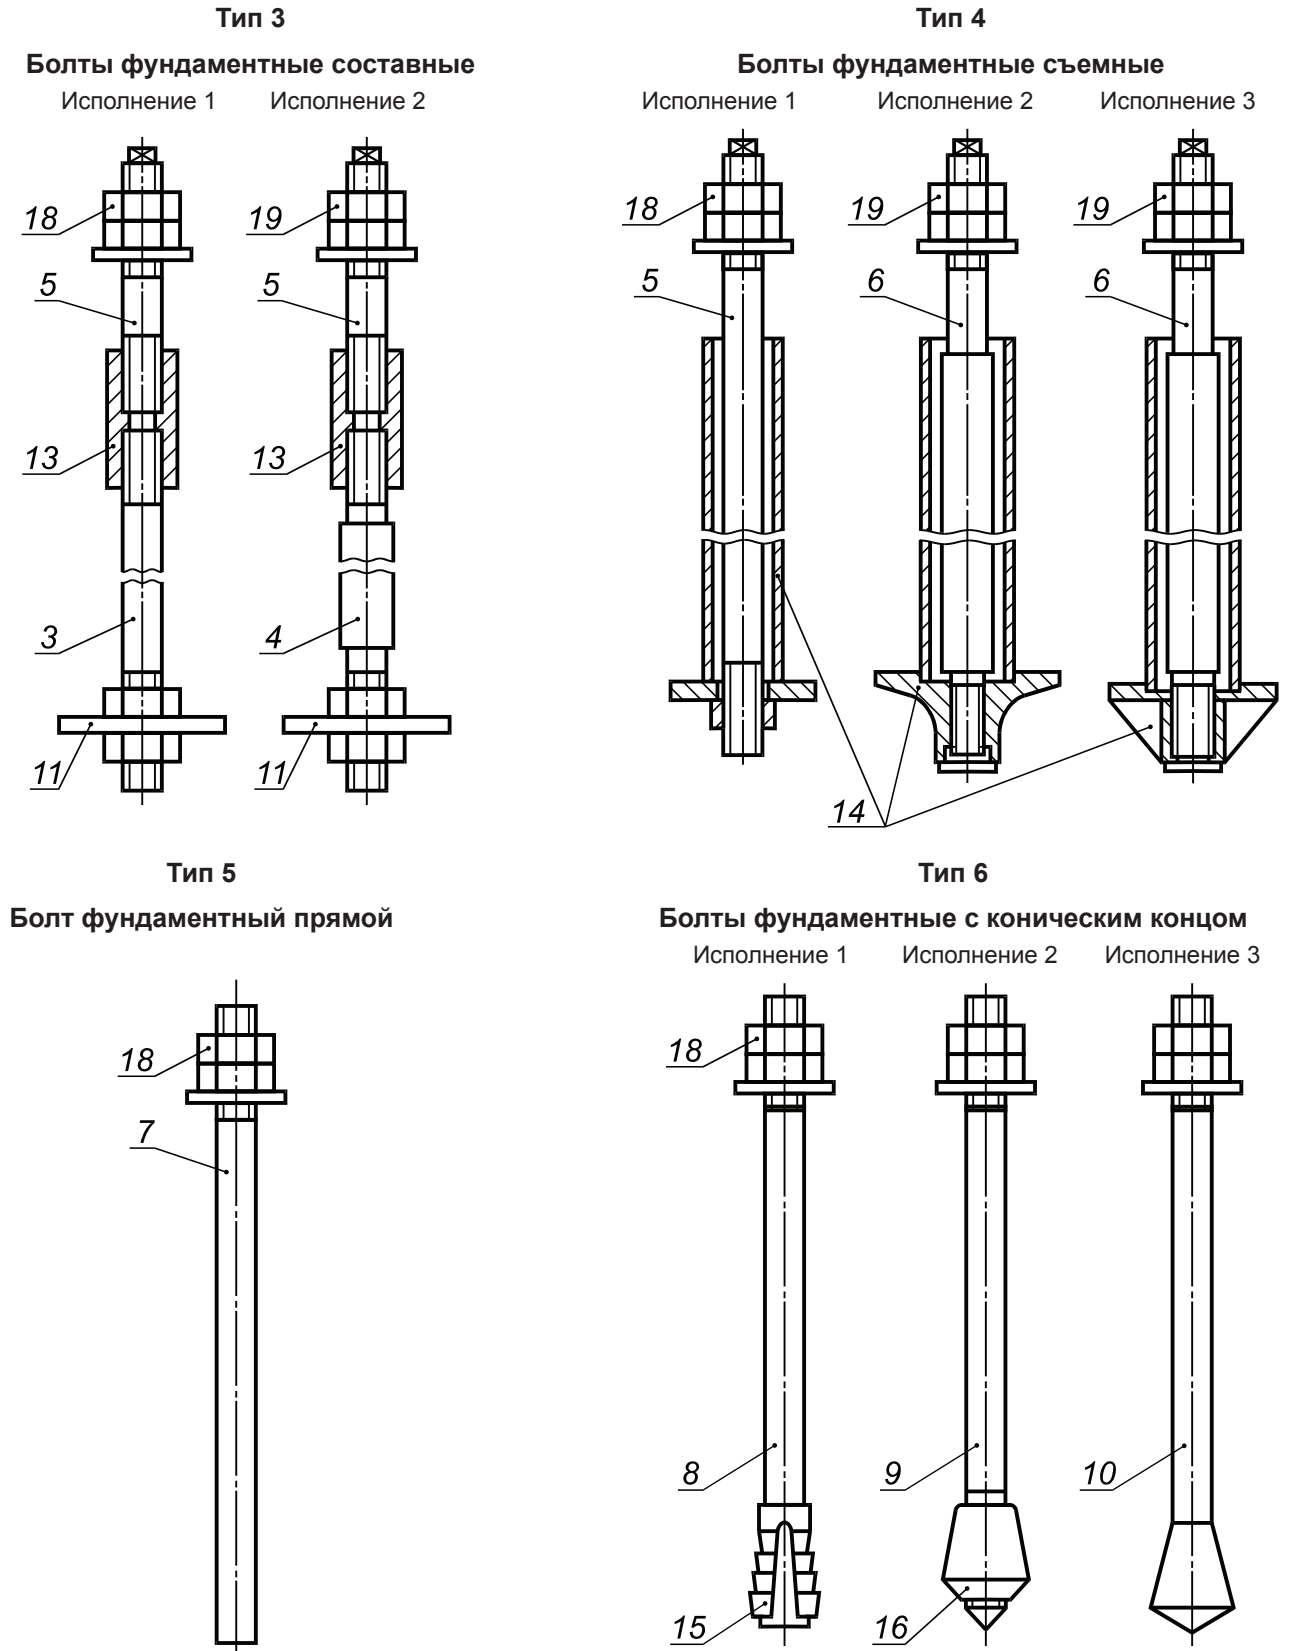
Типы и конструкция фундаментных болтов, лист 1
